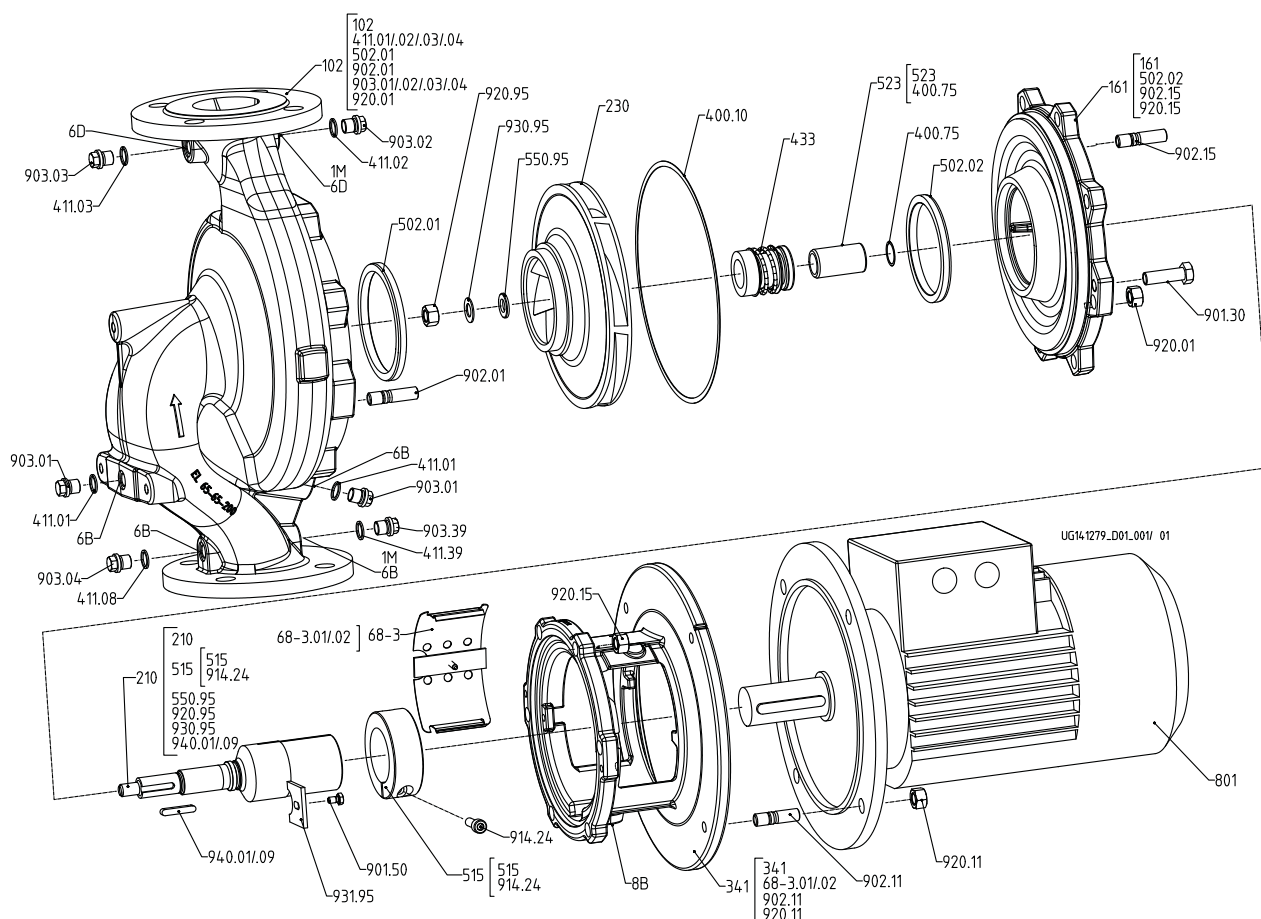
Исполнение с привинчиваемой крышкой корпуса
